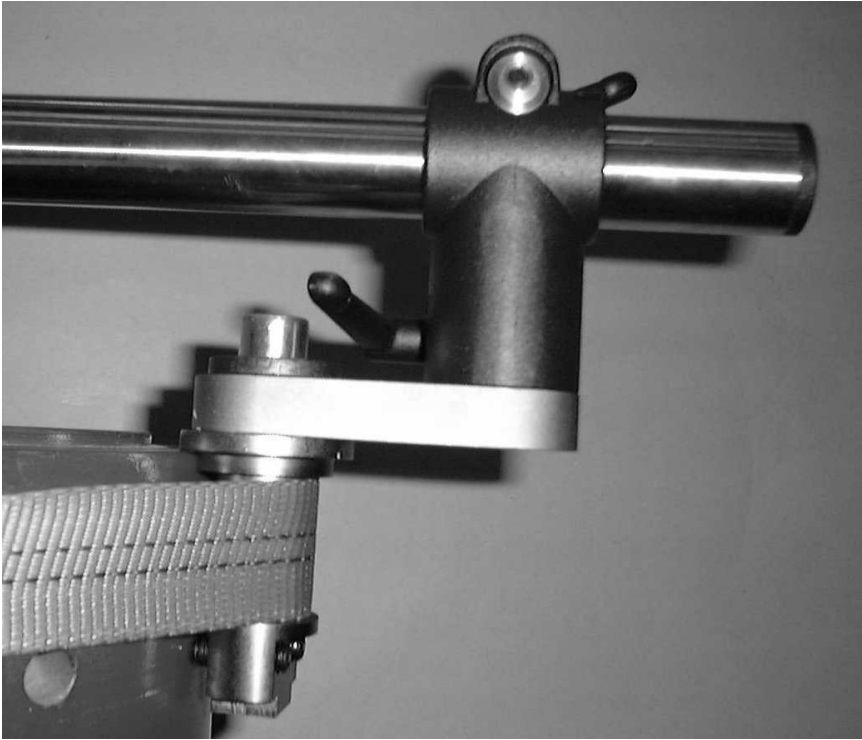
Установка универсального зажимного устройства при помощи приспособления "стойка воротника"
